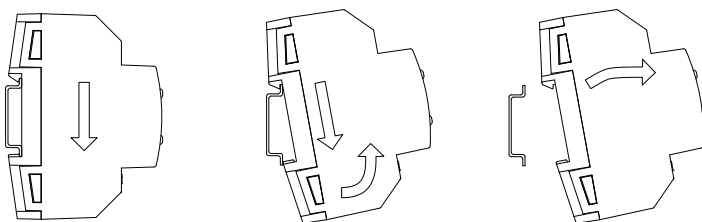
Montaje de DIMinBOX DX4 en carril DIN
